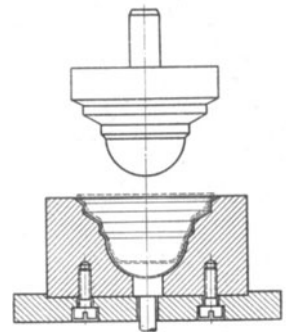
Formschlag- oder Stanzwerkzeug (hier Fertigform).
